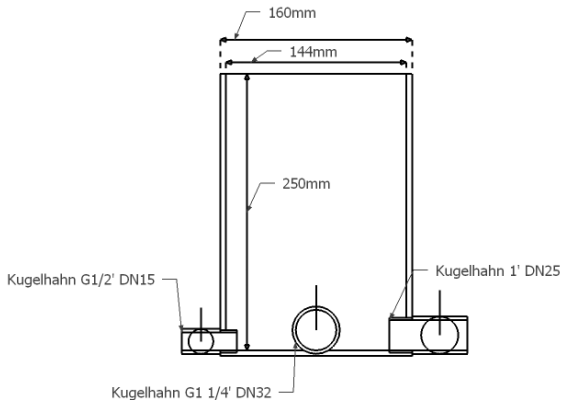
Technische Zeichnung des Versuchszyinders für die Ausflussexperimente, Draufsicht
